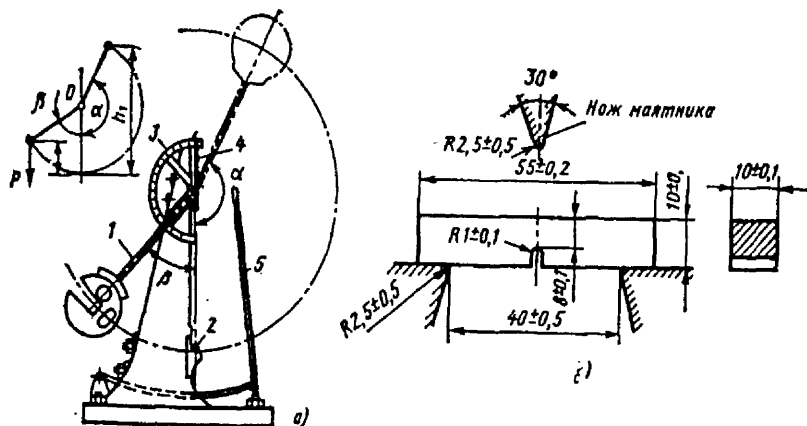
Схема маятникового копра (а) и образца при испытании (б): 1 – маятник; 2 – образец; 3 – шкала; 4 – стрела; 5 – тормоз
